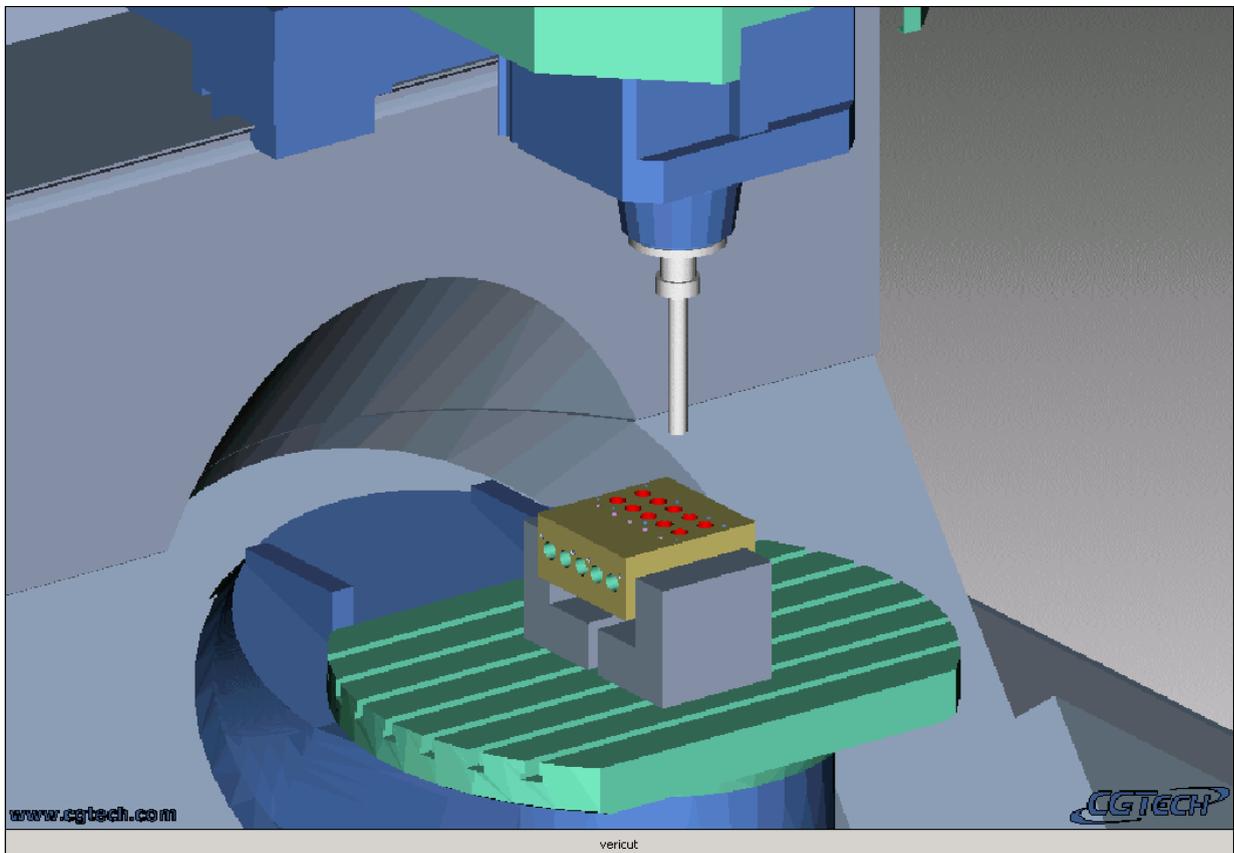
Hydraulikblock in VERCUT mit Spannvorrichtung und Werkzeug
